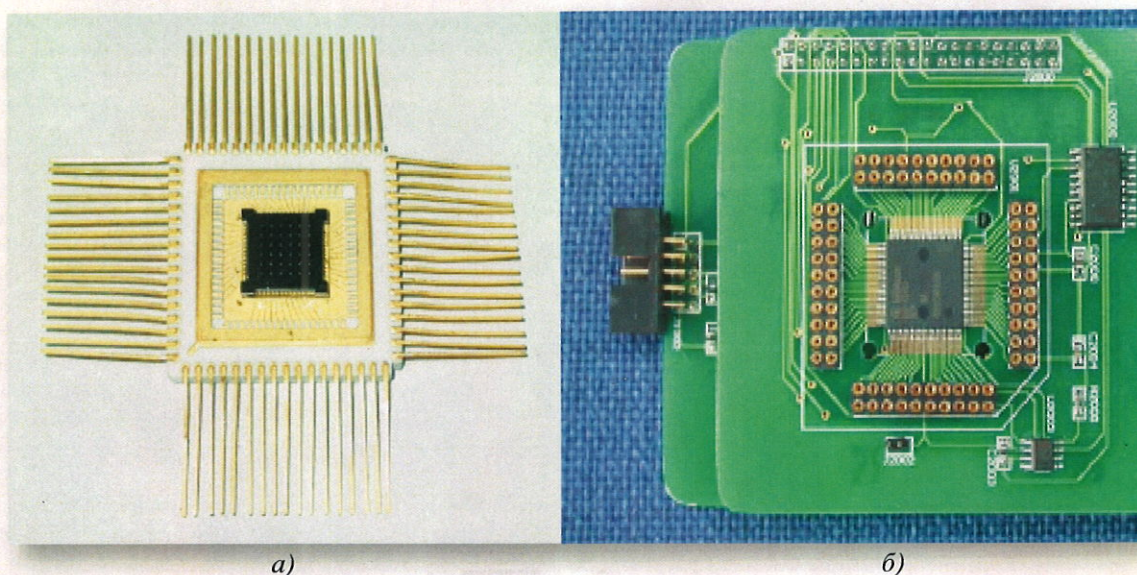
Общий вид комплекса РМДТТ и его вид в сборке для испытаний
